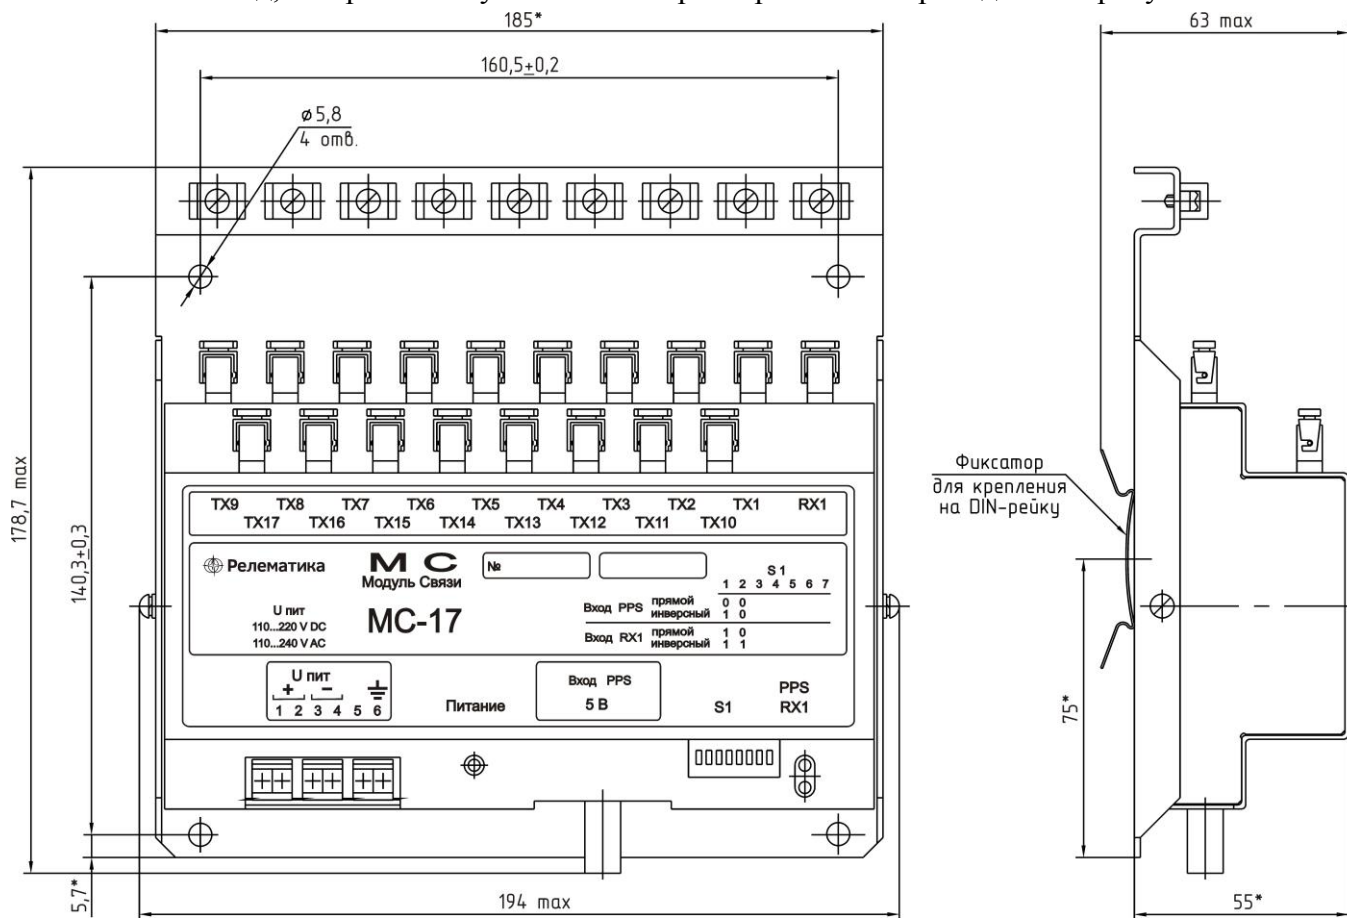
Внешний вид, габаритные и установочные размеры МС-17
